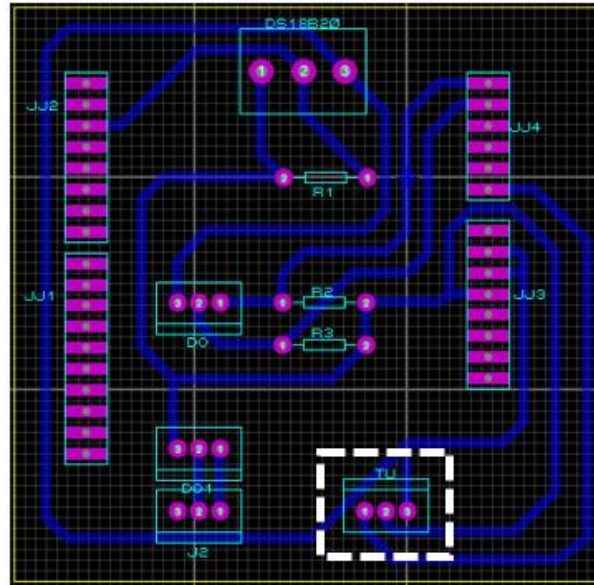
Conexión del sensor de turbidez en el PCB.
